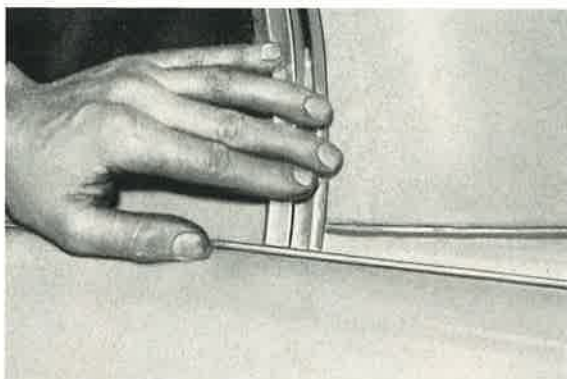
So glatt soll die Regenleiste hinten mit dem Köder für den Hinterradkotflügel abschließen.
